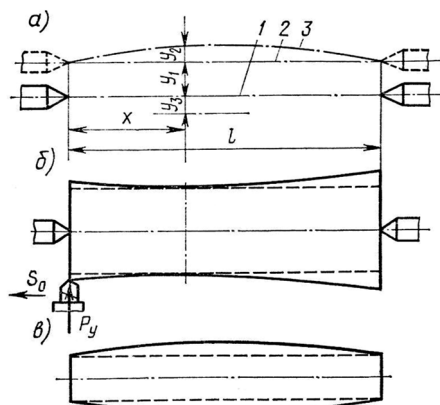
Схема утворення похибок при обточуванні деталі тіла обертання на токарному верстаті
